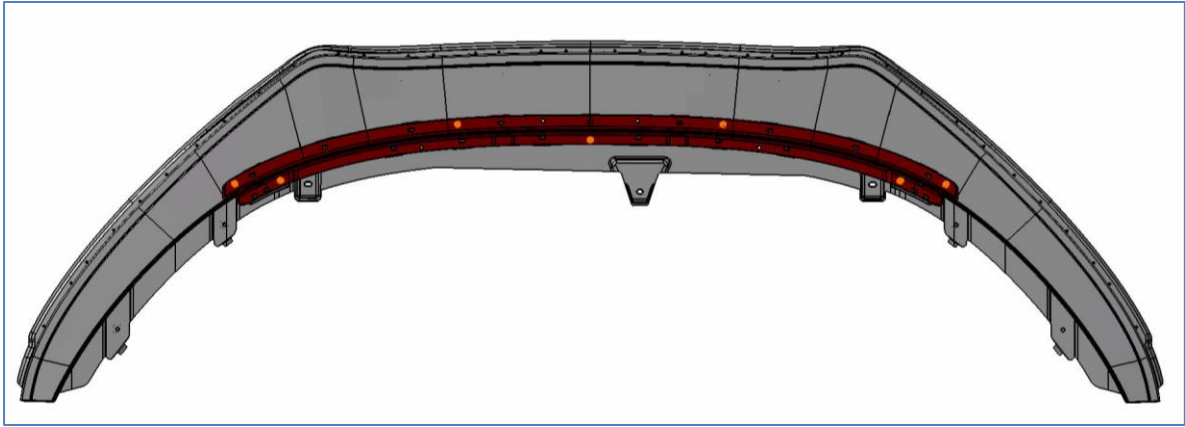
Conjunto spoilerlippe montado, vista en planta
